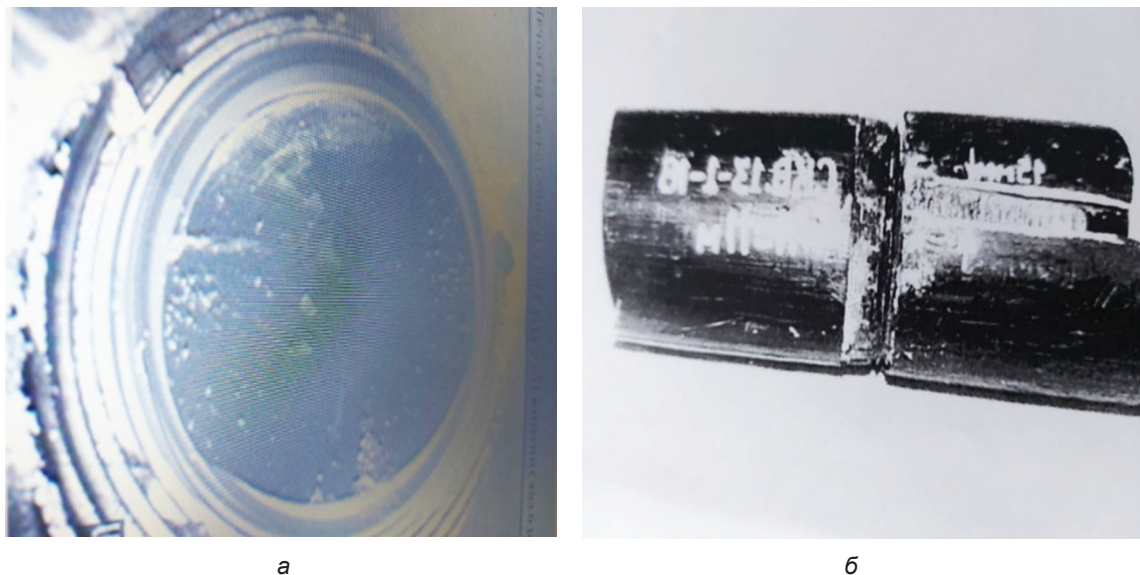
Разрушение резьбового соединения труб ПНД 160×18 при охлаждении ЭК (а) и разрыв резьбового соединения трубы ПНД 110×18 при нагревании ЭК (б) / Fig. 1. Destruction of the threaded connection of HDPE pipes 160×18 during cooling of the EC (а) and rupture of the threaded connection of the HDPE pipe 110×18 when the EC (b) is heated
